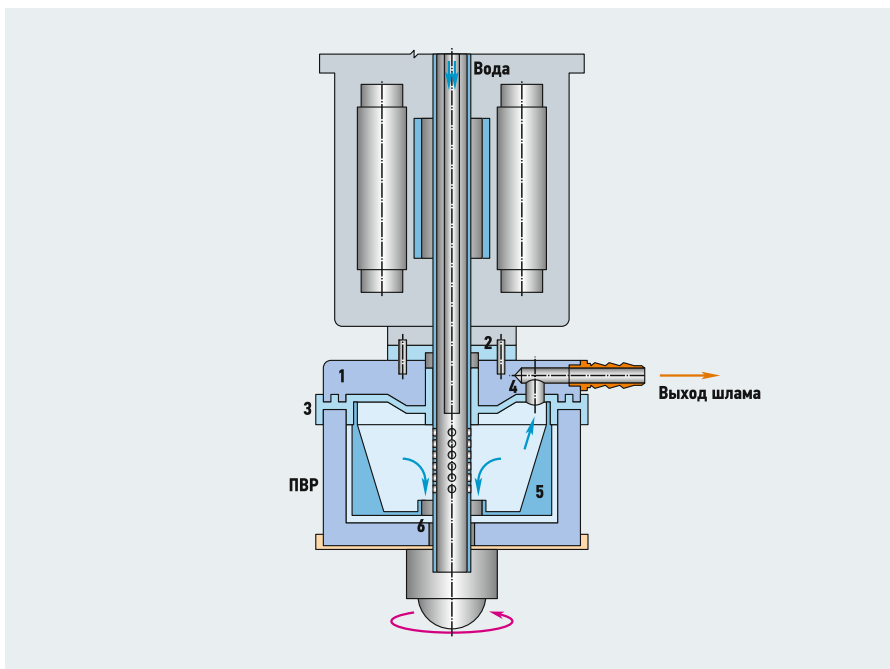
Конструкция ПВР для распыления нефilterованной воды (1 — неподвижная крышка со штуцером для вывода осадка; 2 — стопоры; 3 — верхняя крышка ПВР; 4 — отверстие для вывода шлама; 5 — вкладыш-сепаратор; 6 — центральная кольцевая щель)
